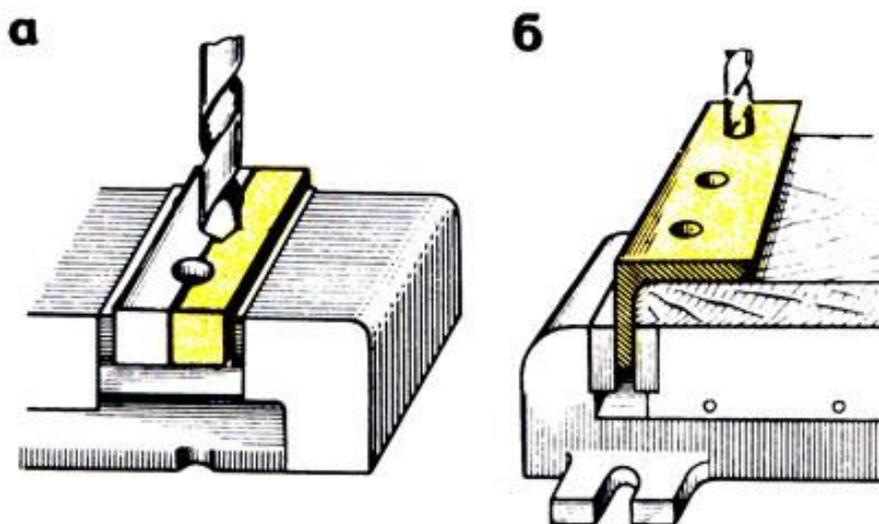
Сверление: а - неполного отверстия при помощи приставной пластинки, б - отверстия в угольнике
